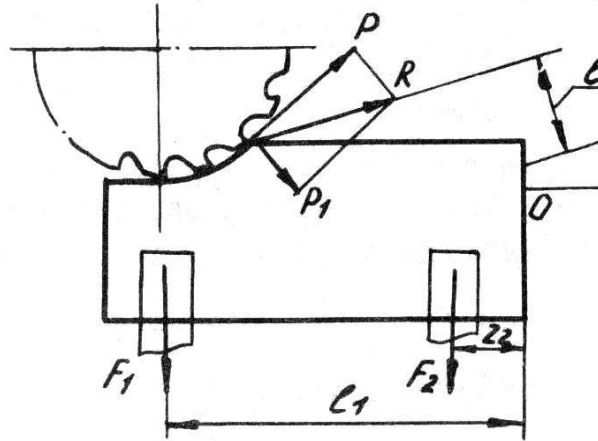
Схема розрахунку сил затиску для фрезерування з прямолінійною подачею
